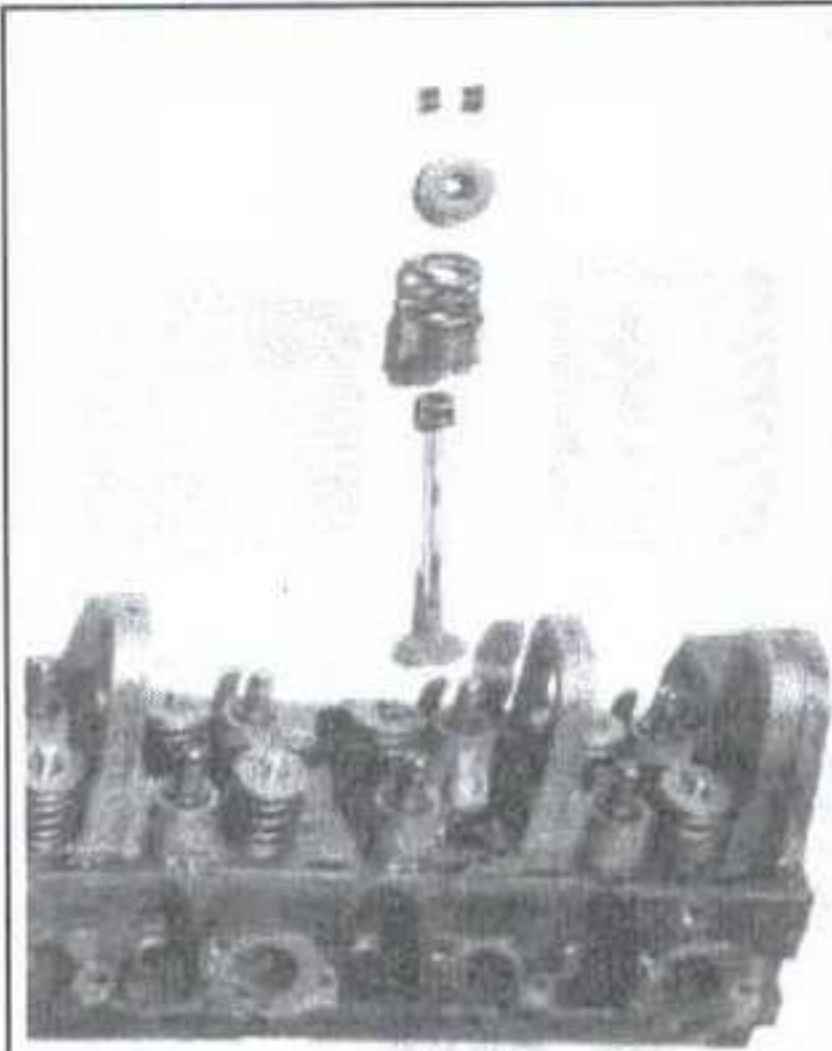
Головка цилиндров с распределительным валом верхнего расположения: клапан, сальник, пружина, тарелка и сухарики
